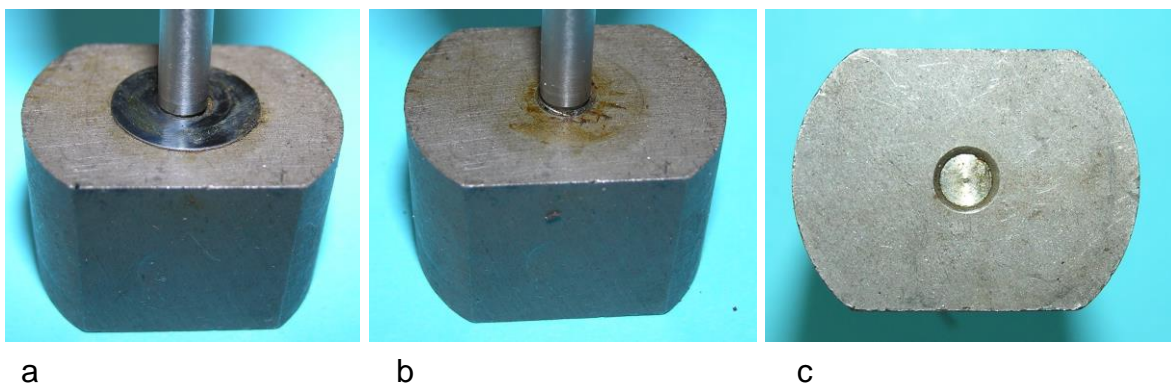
Kraftschlüssiger Einsatz der Welle im zweipoligen AlNi-Magneten: Gewicht mit Welle 100 g, Durchmesser 32 mm, Länge 20 mm, Breite 24 mm
